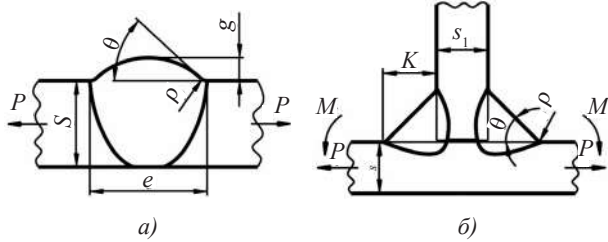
Геометрические параметры сварных швов: а — стыкового; б — углового
